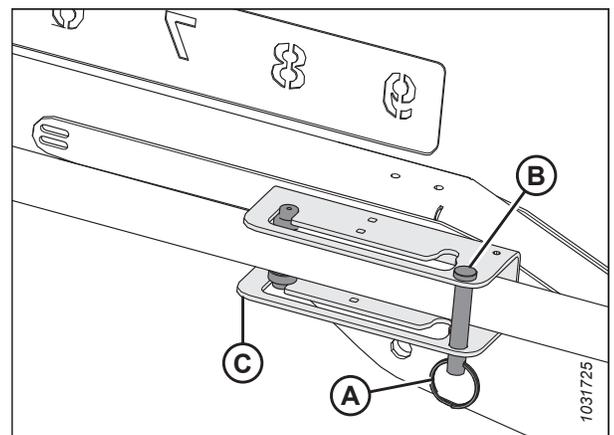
Cilindro del braccio sinistro – Posizione avanzata
